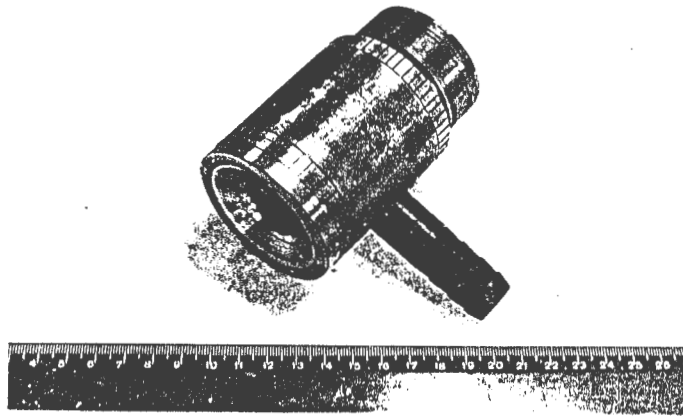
Fotografia do bocal MIG/MAG de soldagem subaquática.
